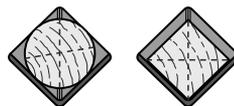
Marque le centre au bout des pièces carrées et cylindriques
